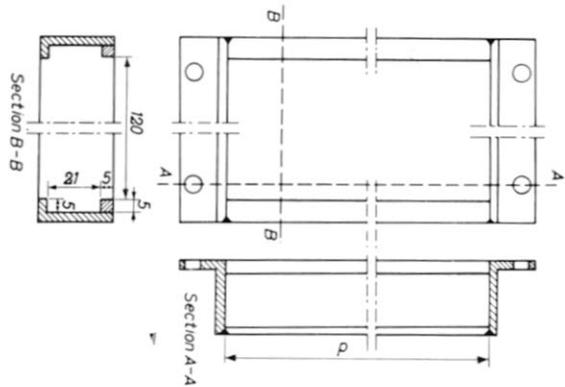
Dimensions du cadre de la Fig. 50. La dimension p dépend du nombre de connecteurs.
